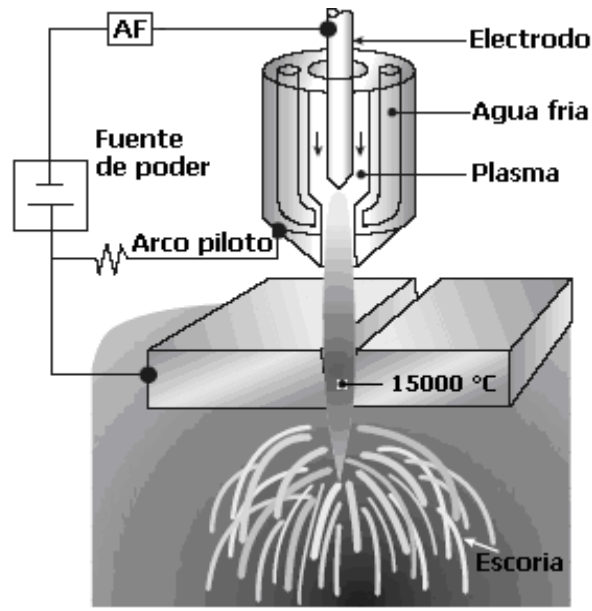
Esquema. Proceso soldadura arco con plasma.
